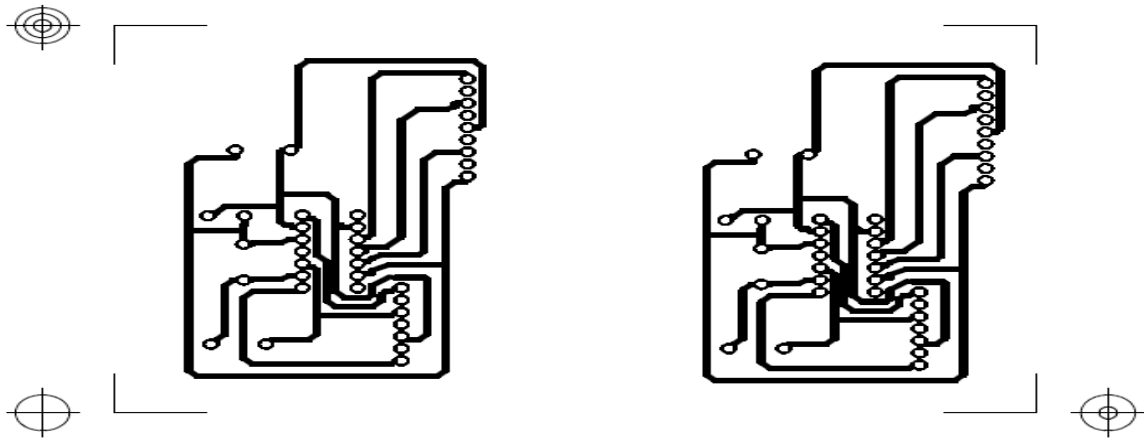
Vista de Impresión de los Drivers Terminados en el UltiBoard.
